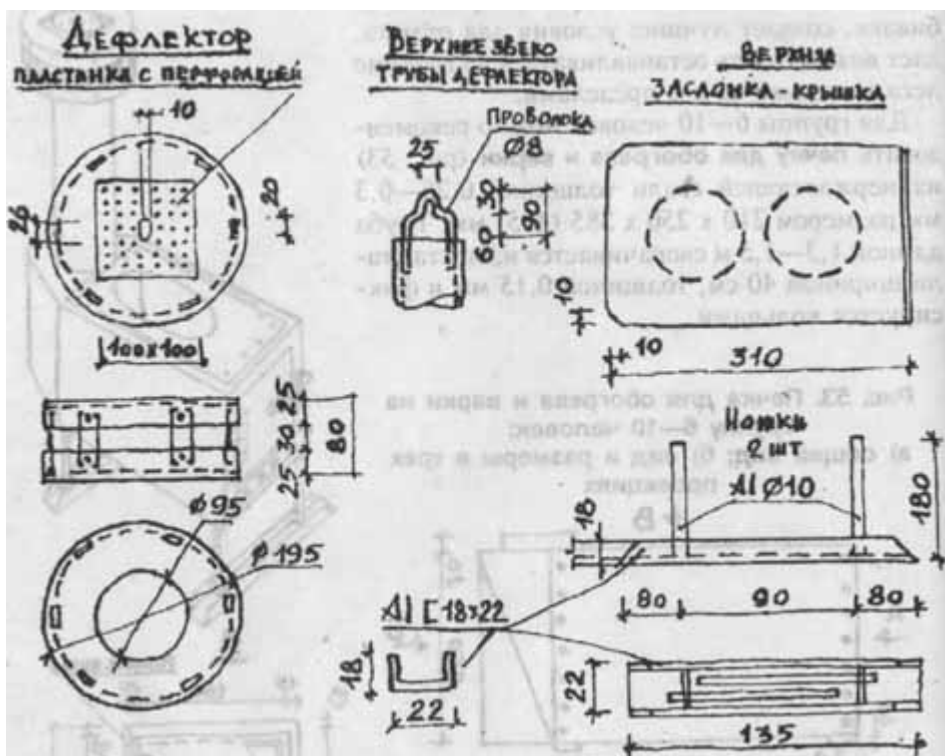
Печка для обогрева и варки на группу 6—10 человек: в) детализировка
